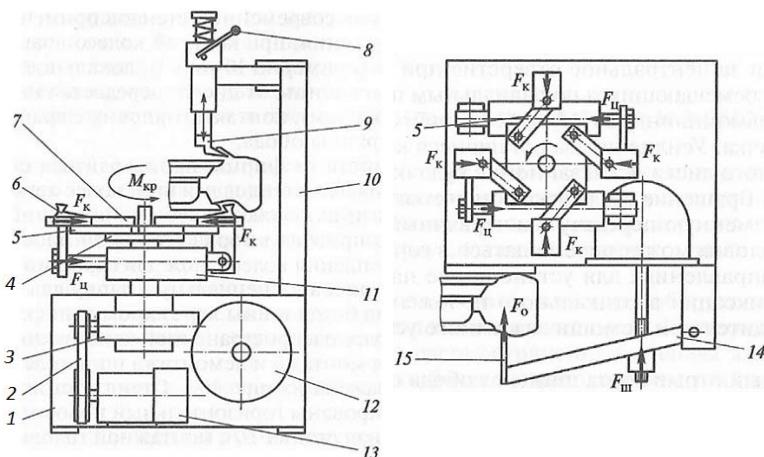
Устройство шиномонтажного стенда: 1 – каркас; 2 – ременная передача; 3 – червячный редуктор; 4 – диск; 5 – тяга; 6 – кулачок; 7 – монтажный стол; 8 – рукоятка фиксации вертикального положения монтажной головки; 9 – монтажная головка; 10 – монтажная стойка; 11 – пневмоцилиндр привода кулачков; 12 – пневмокамера привода механизма отжима борта шины; 13 – электродвигатель; 14 – рычаг механизма отжима борта шины; 15 – отжимная лопатка; M_{kp} – крутящий момент, приложенный к поворотному монтажному столу; F_u – сила на штоке пневмоцилиндра привода кулачков; F_k – сила прижатия кулачков к закраине диска; F_o – отрывная сила на отжимной лопатке; F_{iii} – сила на штоке пневмокамеры привода отжимной лопатки
